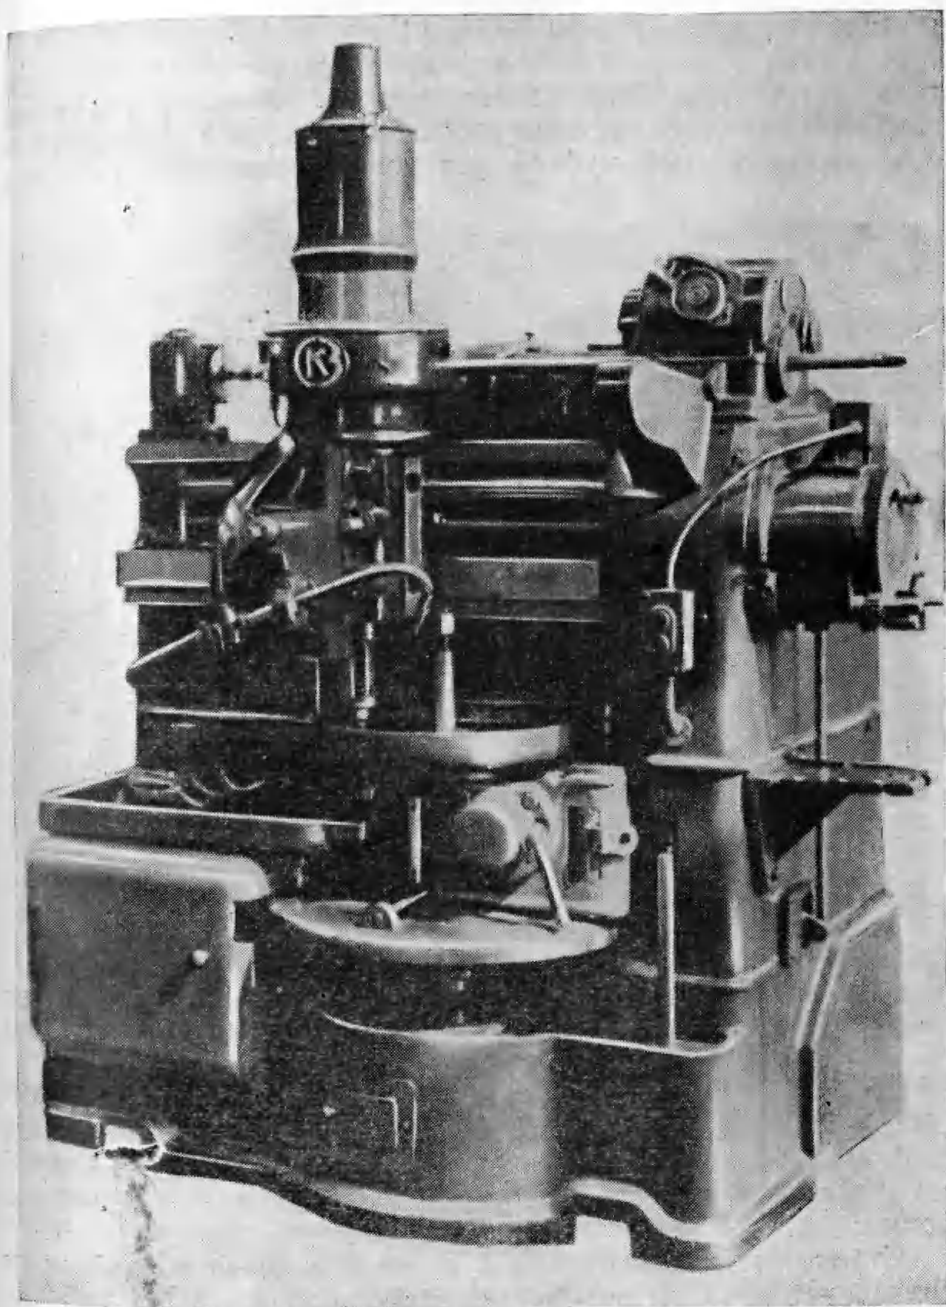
Зубофрезерный станок универсального типа для нарезания цилиндрических колес червячной фрезой, мод. 532, диаметр нарезаемой шестерни 750 мм, модуль 8 мм (завод „Комсомолец“).
